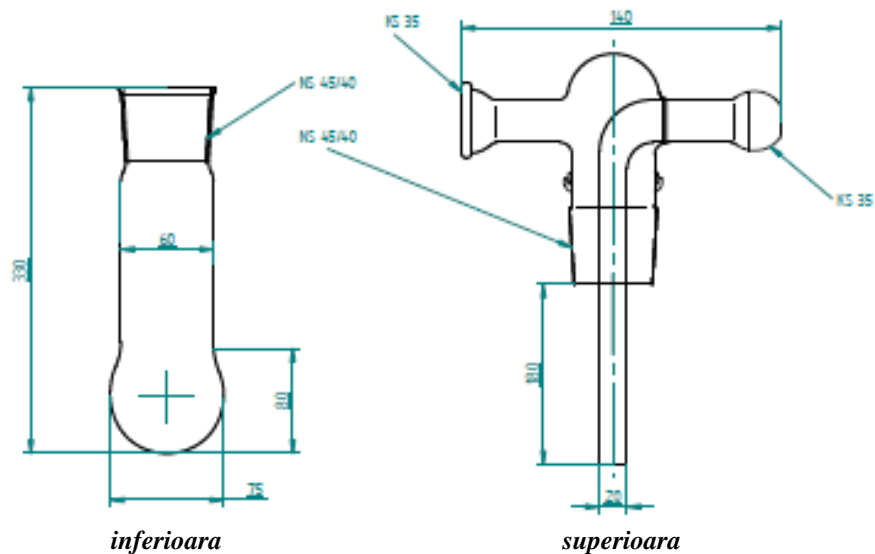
Piese trapa de racire - Componenta si dimensiuni
